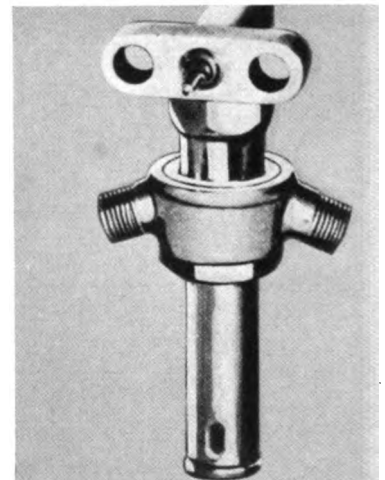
Kombinierte Einspritzpumpe und -Düse
